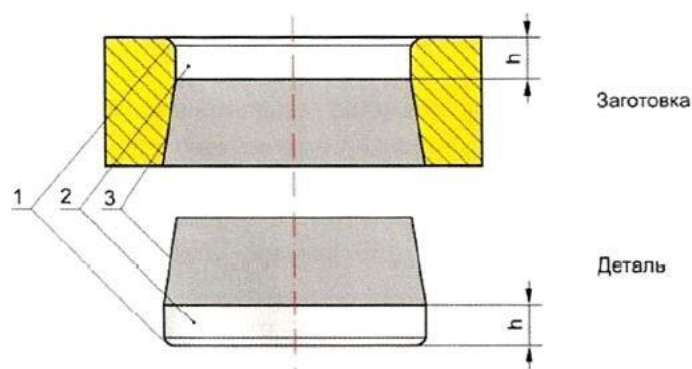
Характерные участки боковой поверхности детали и заготовки после вырубki
